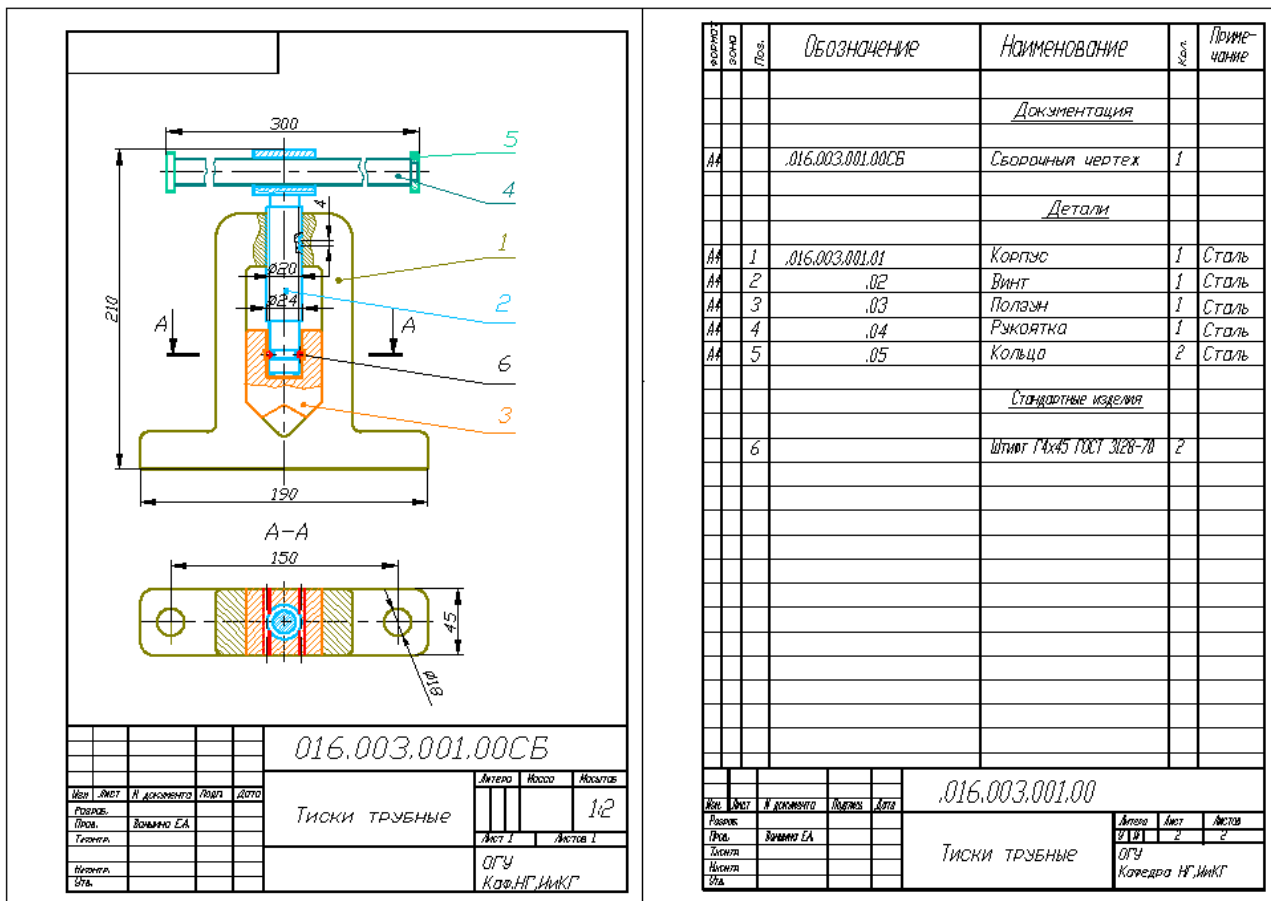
Сборочный чертеж «Тиски трубные».
